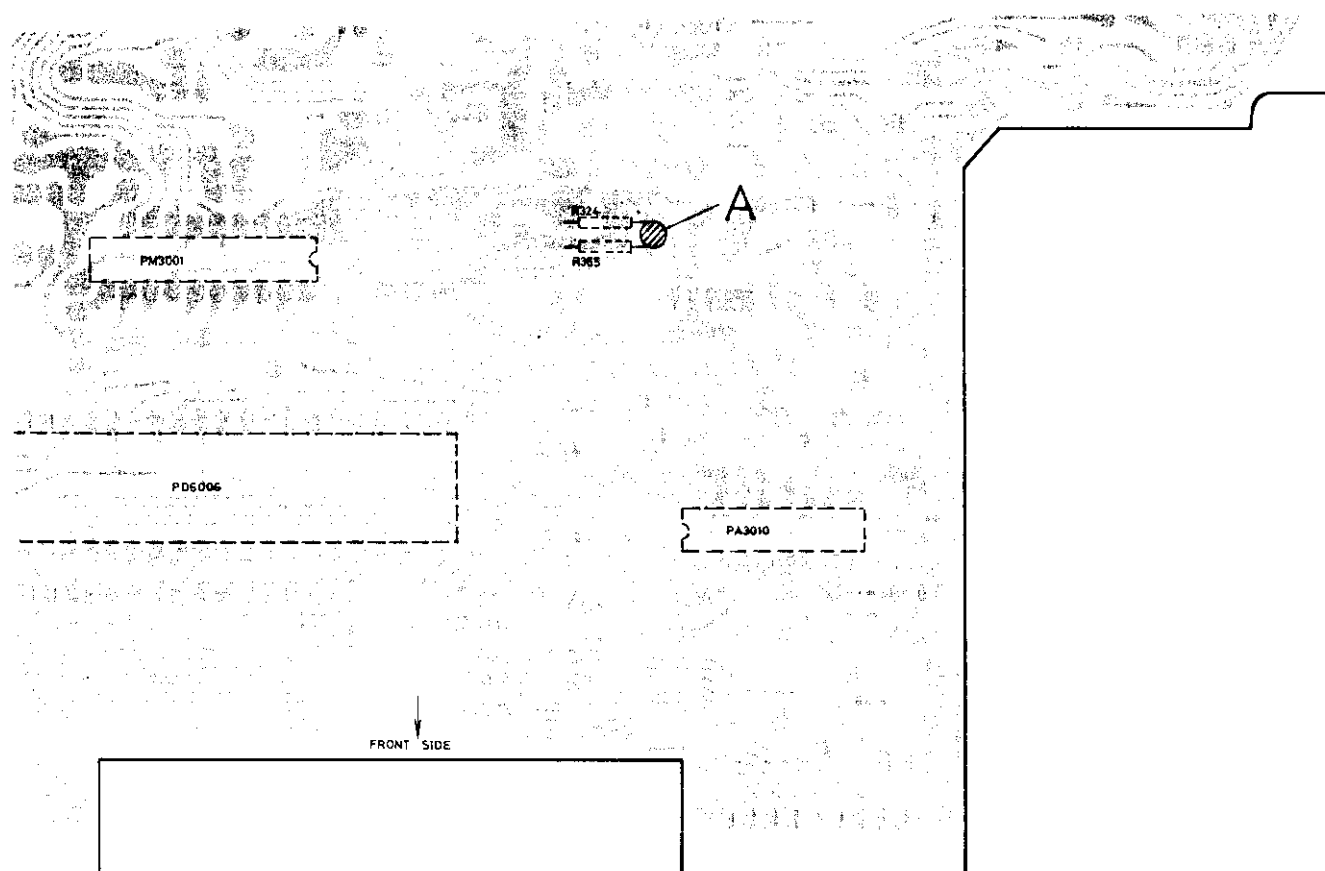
Punto de soldadura (lado de la lámina del ensamblaje de control)
